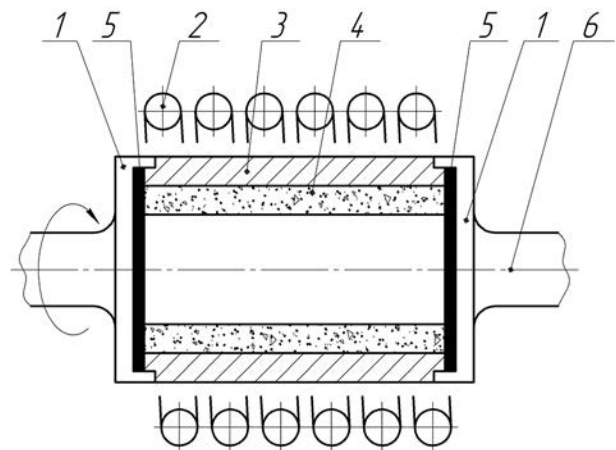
Принципиальная схема центробежной индукционной наплавки: 1 — зажимные крышки; 2 — индуктор; 3 — деталь; 4 — наплавляемая шихта; 5 — антипригарные прокладки; 6 — ось детали
